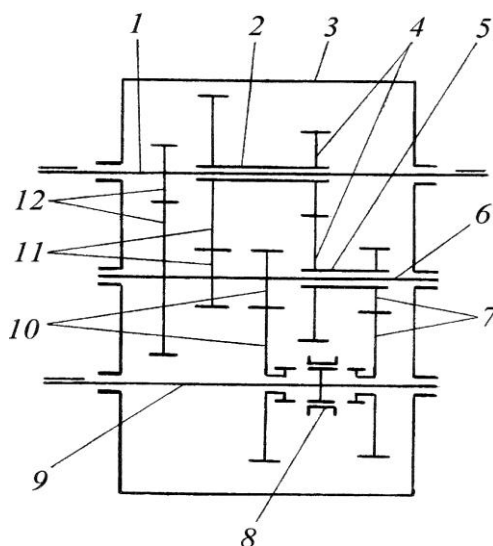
Кинематическая схема ходоуменьшителя: 1 — ведущий вал; 2,5 — свободно вращающиеся блоки шестерен; 3 — корпус; 4,7,10,11,12 — пары шестерен постоянного зацепления; 6 — промежуточный вал; 8 — блокировочная муфта; 9 — ведомый вал
